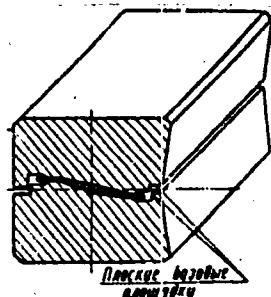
Эскиз штампа для поковки лопатки компрессора с плоскими площадками.
